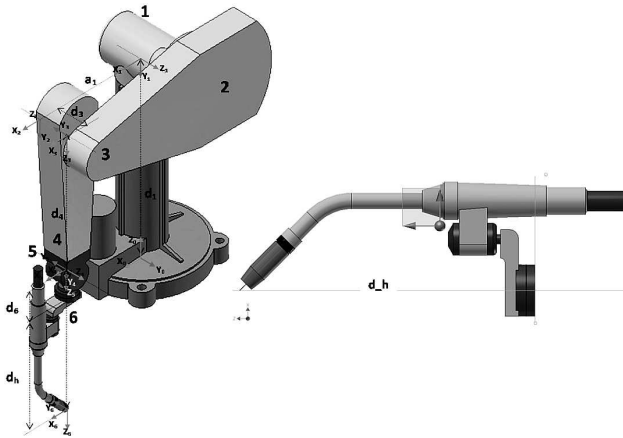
Esquema PUMA 560 y pistola soldadura de arco TOUGH GUN G2
